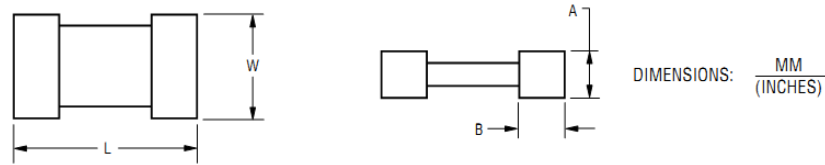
Габарити корпусу RC1206 J , F
